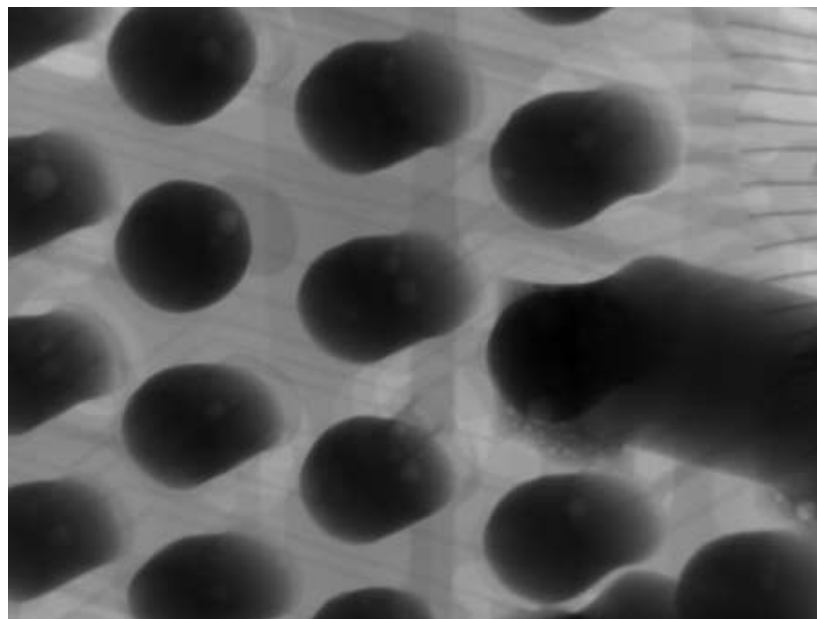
Дефект пайки мікросхеми BGA
